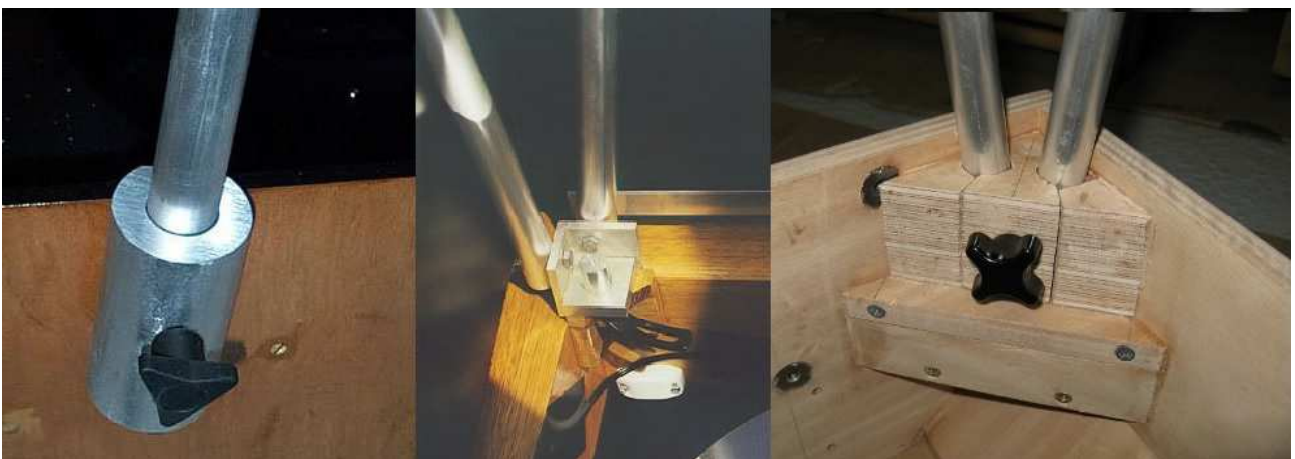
Exemples de fixations des tubes à la caisse du primaire
